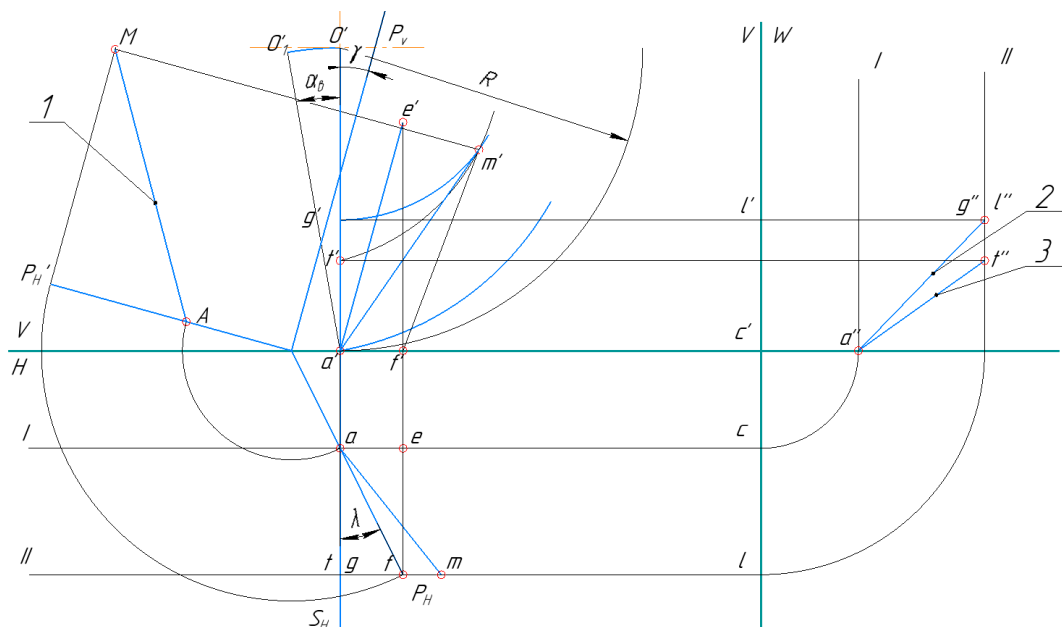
Профільювання фрез для обробки циліндричних поверхонь.[4]
